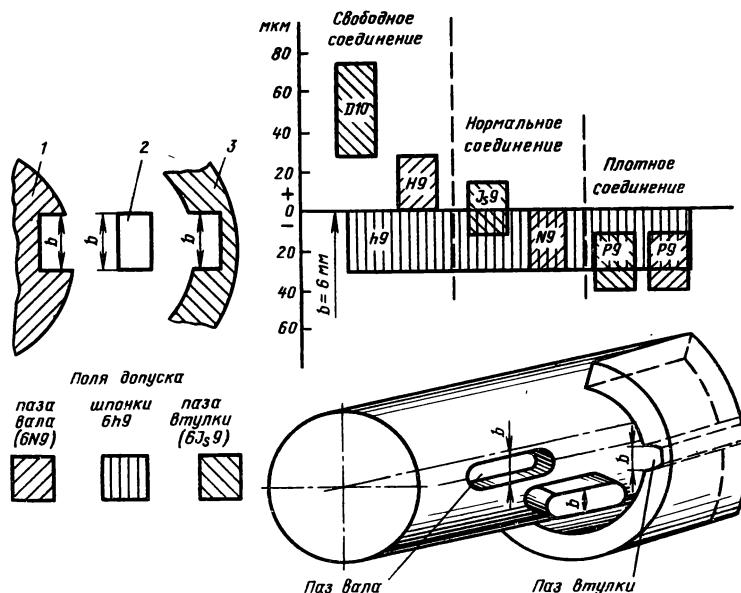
Схема расположения полей допусков шпоночного соединения с призматической шпонкой:
